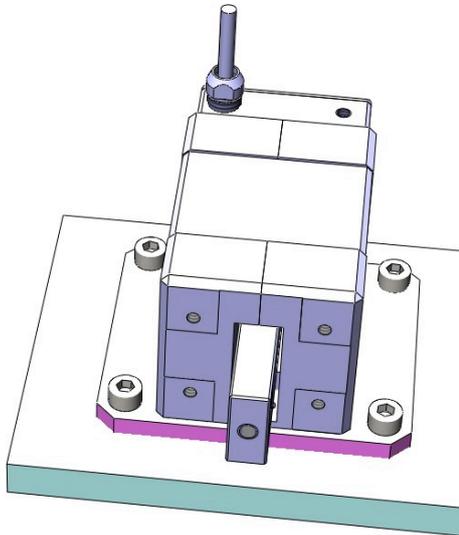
Beispiel für Montage mittels Montageflansch A (räumliche Ansicht)
